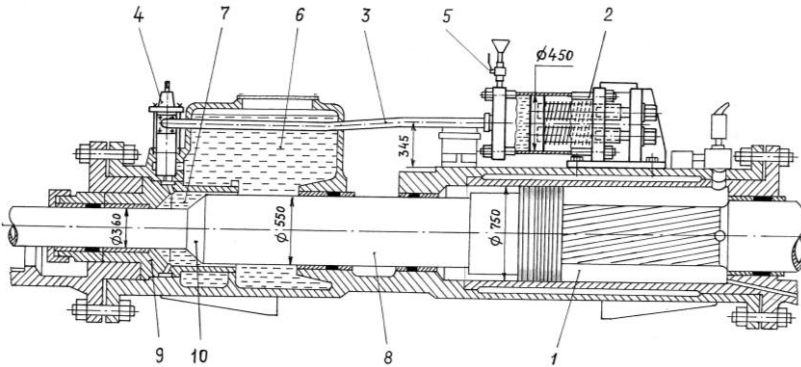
Повітряний робочий циліндр подавального апарата з пружино-гідравлічним буфером: 1 – камера повітряного циліндра (поршнева порожнина); 2 – буфер; 3 – трубопровід; 4 – запірний вентиль; 5 – шаровий кран; 6 – водяна камера; 7 – камера гальмування; 8 – шпиндель (плунжер); 9 – гальмівна втулка; 10 – уступ шпинделя.
